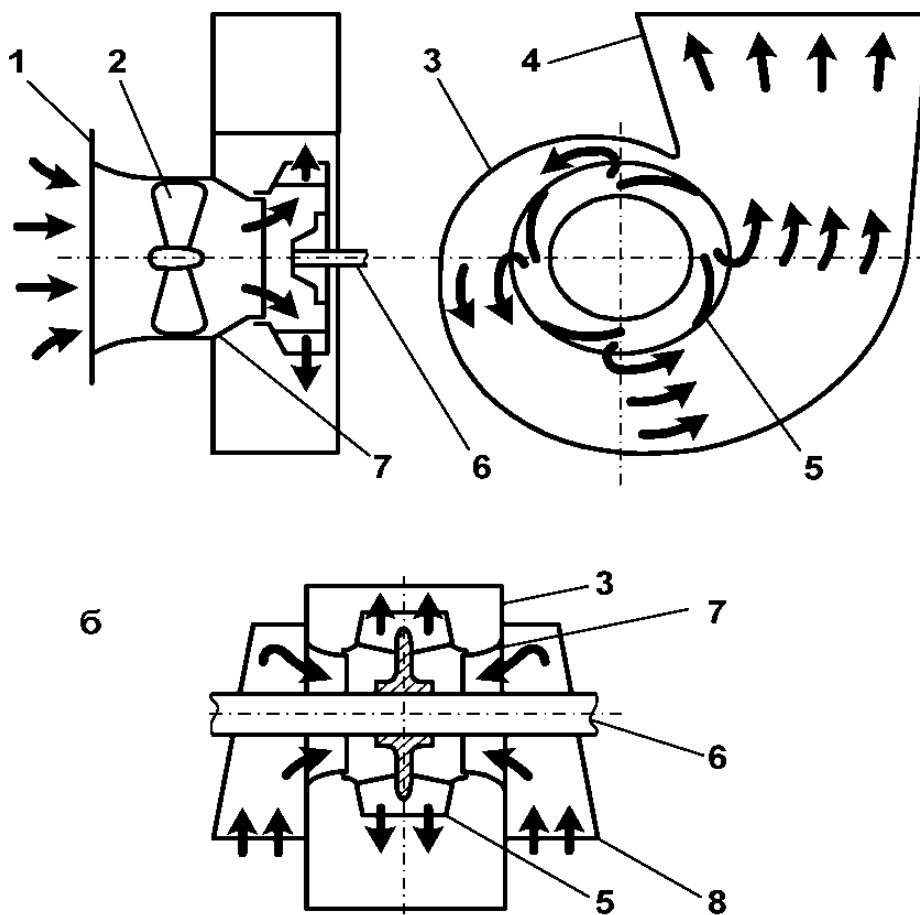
Принципиальные схемы центробежных вентиляторов: а - одностороннего всасывания; б - двухстороннего всасывания. 1 - коллектор; 2 - направляющий аппарат; 3 - кожух; 4 - диффузор; 5 - рабочее колесо; 6 - вал; 7 - уплотнительная втулка; 8 - подводящая коробка
